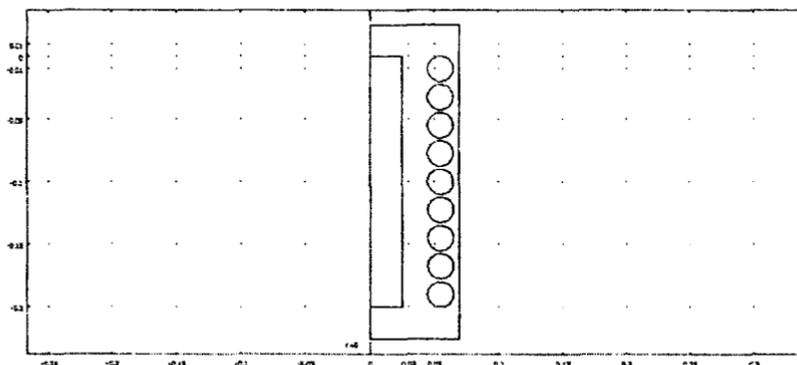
Расчетная схема «индуктор – заготовка»
